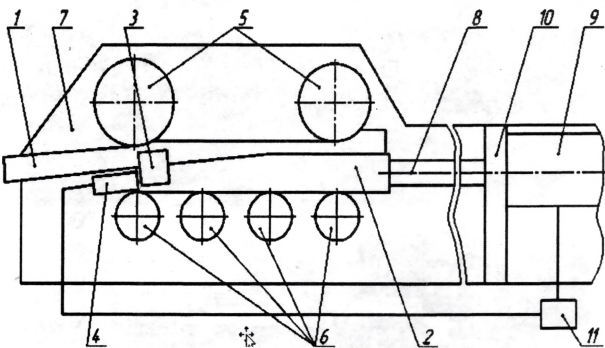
Принципиальная схема стана для прокатки заготовок направляющих элементов пневмоподвески: 1 — заготовка; 2 — оправка; 3 — зажим; 4 — гидроцилиндр зажима; 5 — валки; 6 — опорные ролики; 7 — станина клетки; 8 — шток главного гидроцилиндра; 9 — главный гидроцилиндр; 10 — станина привода
